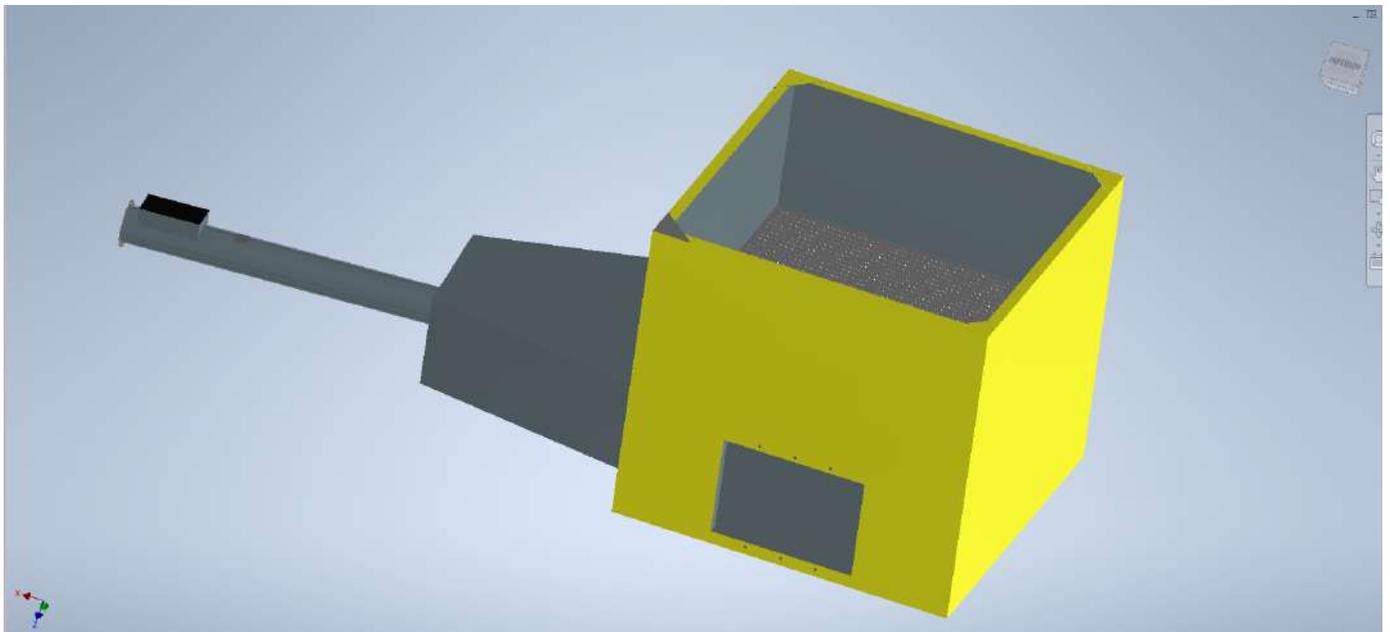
Esquema del diseño la secadora de cacao, fuente: El autor.
